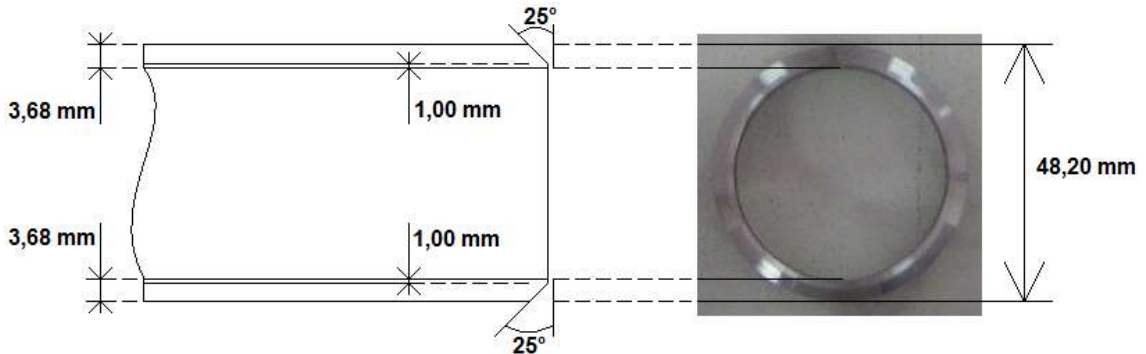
Detalhamento do chanfro utilizado na preparação para soldagem.
